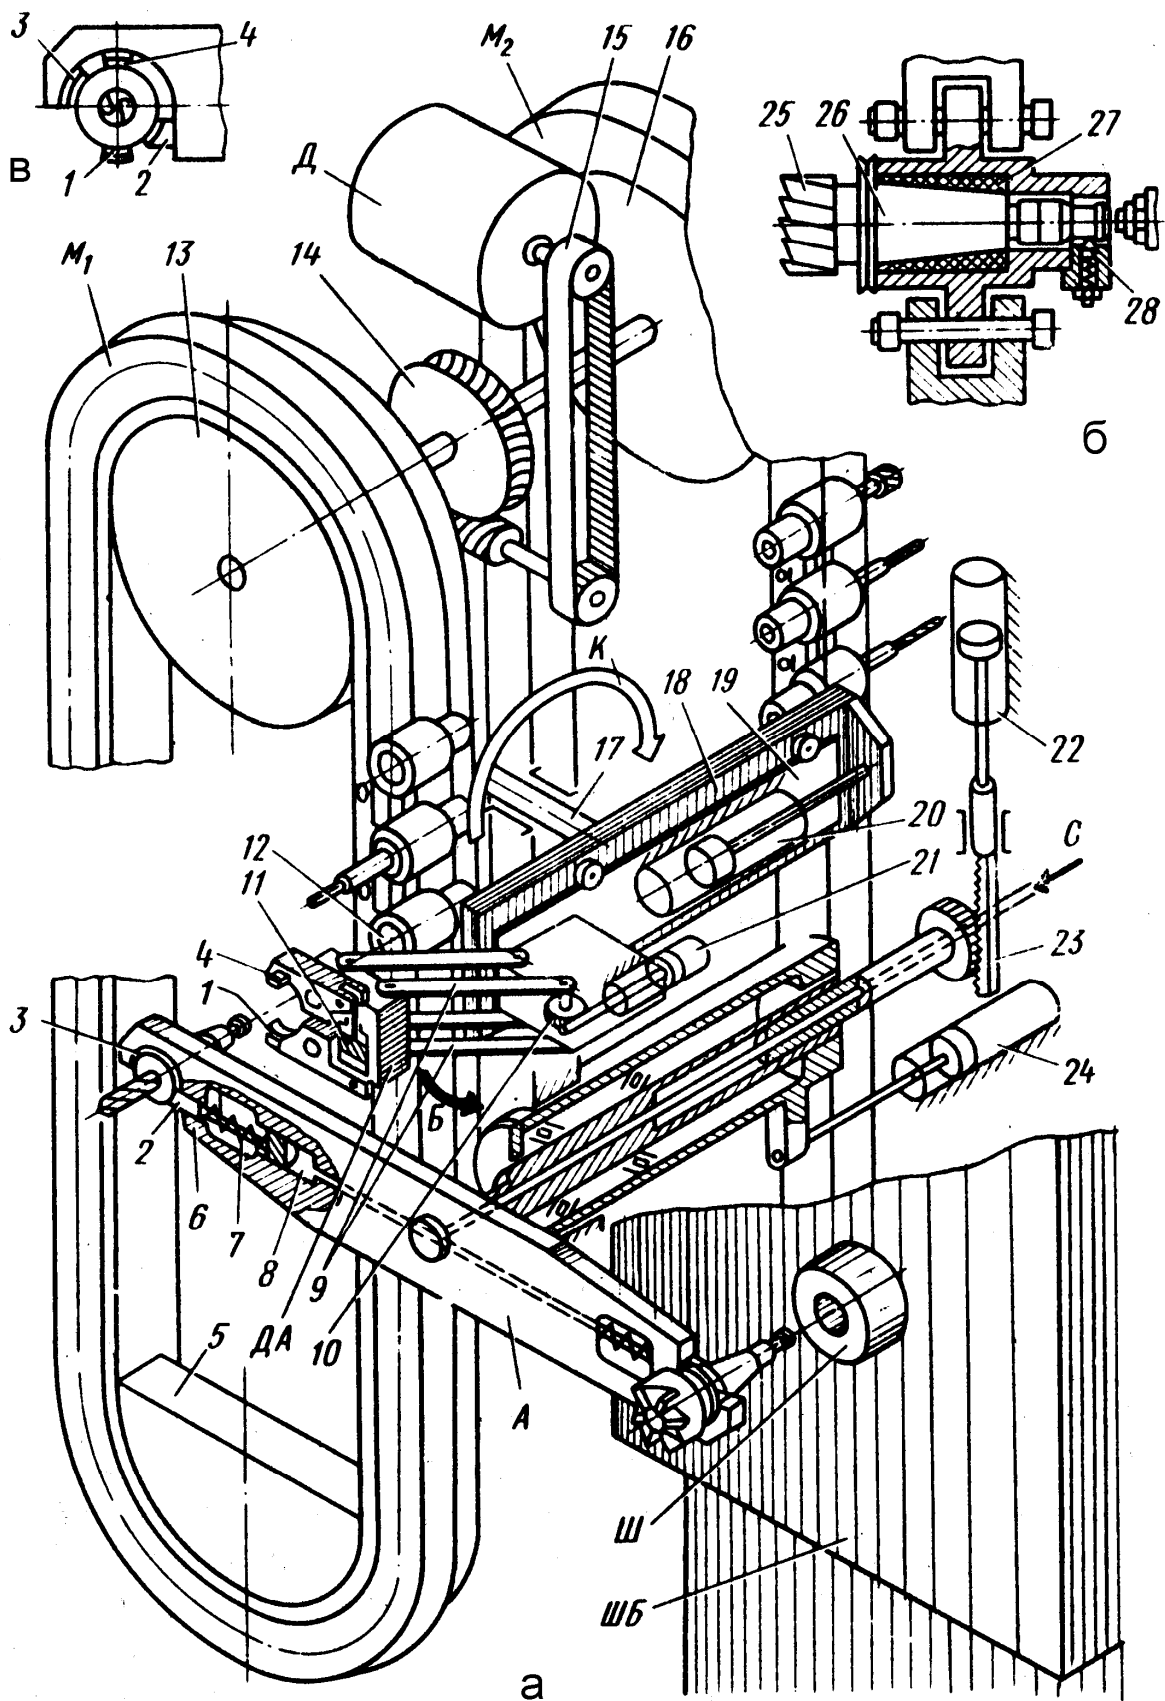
Пристрій АЗІ для БВ з двома магазинами
